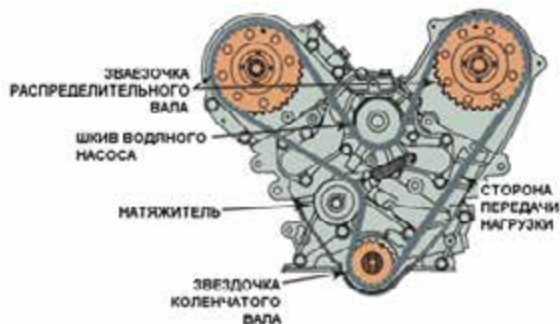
Обе метки на распределительных валах этого двигателя должны быть совмещены с ответными метками на головках цилиндров, а метка на коленчатом валу с соответствующей меткой на крышке картера блока цилиндров. Ременный привод ГРМ приводит во вращение водяной циркуляционный насос (помпу); источник: *Pearson Education, Inc.
